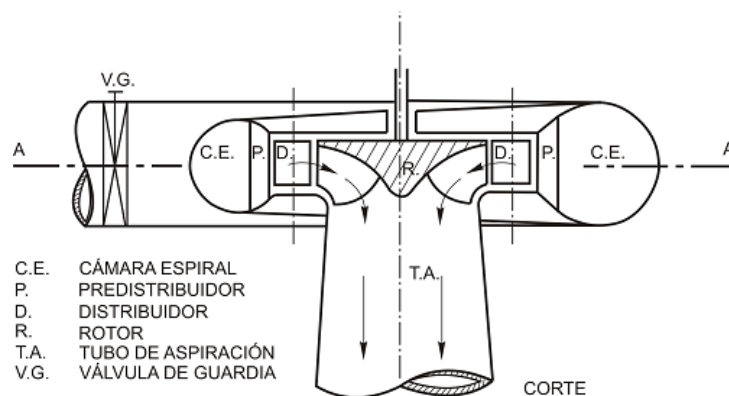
| Corte según un plano meridiano (plano B-B)
